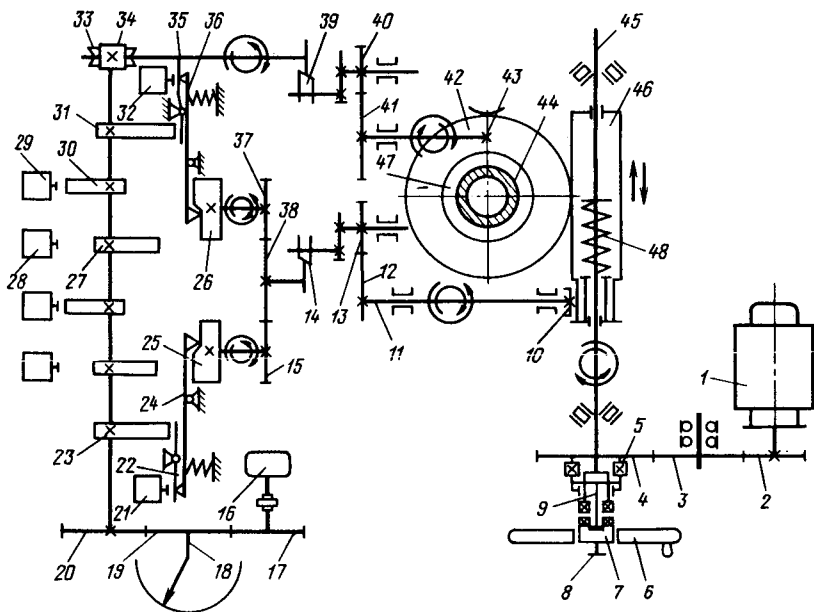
Кинематическая схема унифицированных электроприводов задвижек: 1 — электродвигатель; 2, 3, 4 — колеса; 5 — муфта; 6 — маховик; 7 — кулачковая втулка; 8 — ручка; 9 — шток; 10, 24, 36 — рычаги; 11 — ось; 12 — зубчатый сектор; 13, 15, 37, 38 — цилиндрические колеса; 14, 39 — вилки; 16 — потенциометр; 17 — колесо; 18 — стрелка местного указателя; 19, 20 — шестерни; 21, 28, 29, 32 — микропереключатели; 22, 35, 48 — пружины; 23, 31 — блокировочные кулачки; 25, 26 — моментные кулачки; 27, 30 — кулачки; 33, 42, 43 — червячные колеса; 34 — червяк; 40, 41 — цилиндрические шестерни; 44 — приводной вал; 45 — шлицевой вал; 46, 47 — червяки; 48 — пружина
